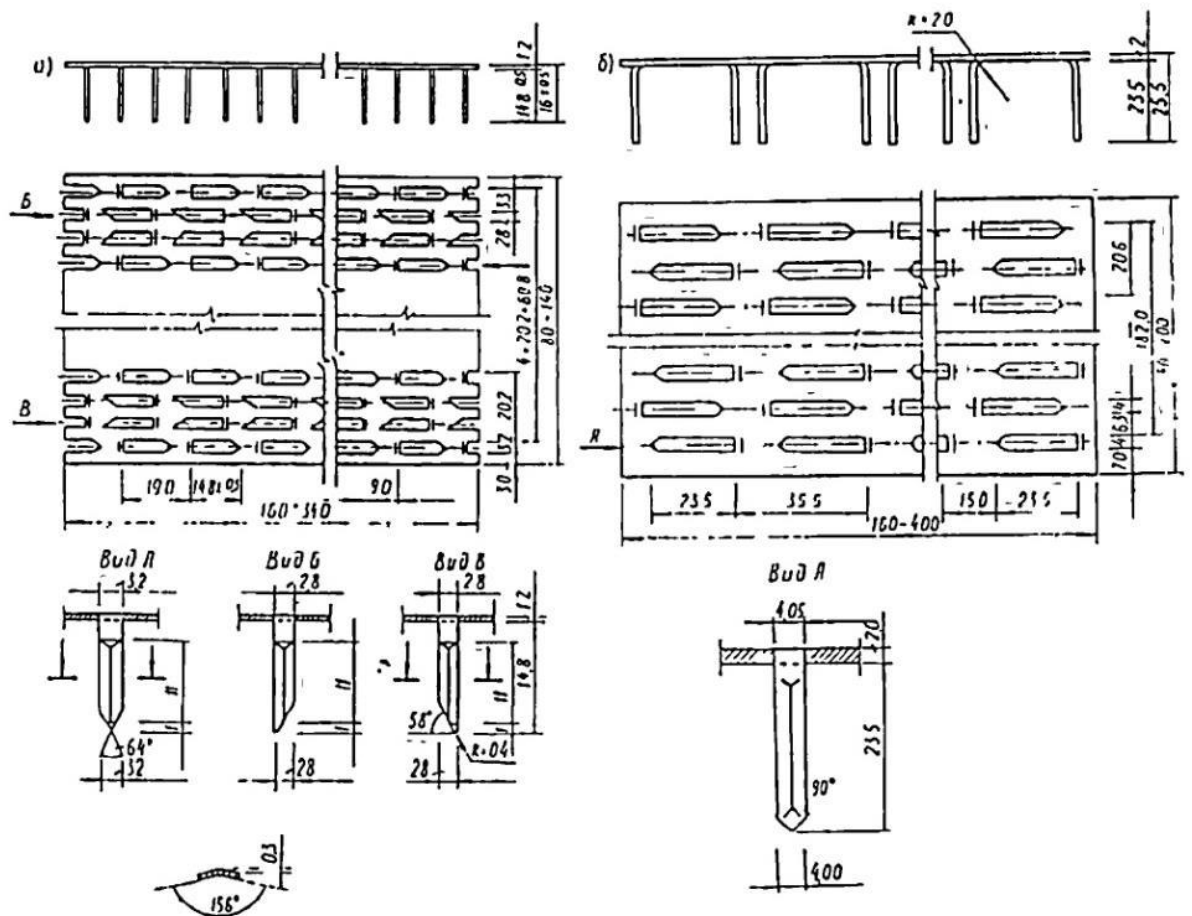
Металлическая зубчатая пластина: а – МЗП-1,2; б – МЗП-2
